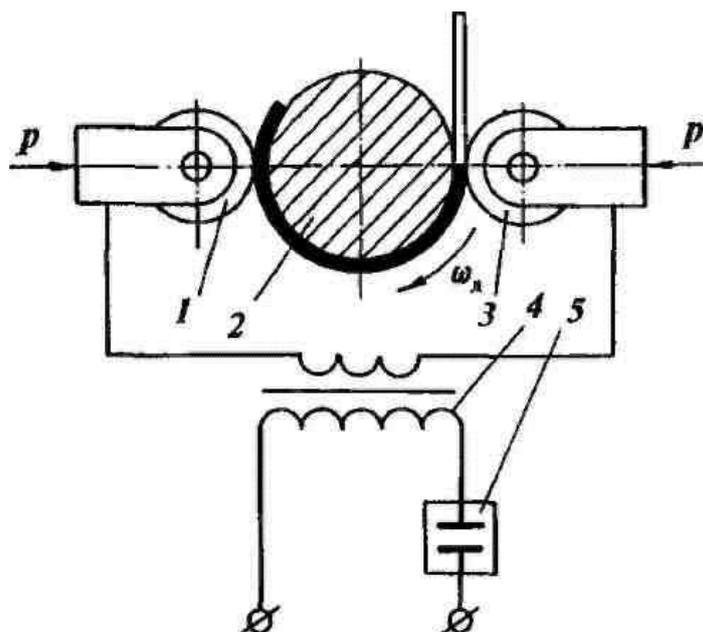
Схема электроконтактной приварки ленты: 1 и 3 – ролики; 2 – восстанавливаемая деталь; 4 – трансформатор; 5 – контактор
